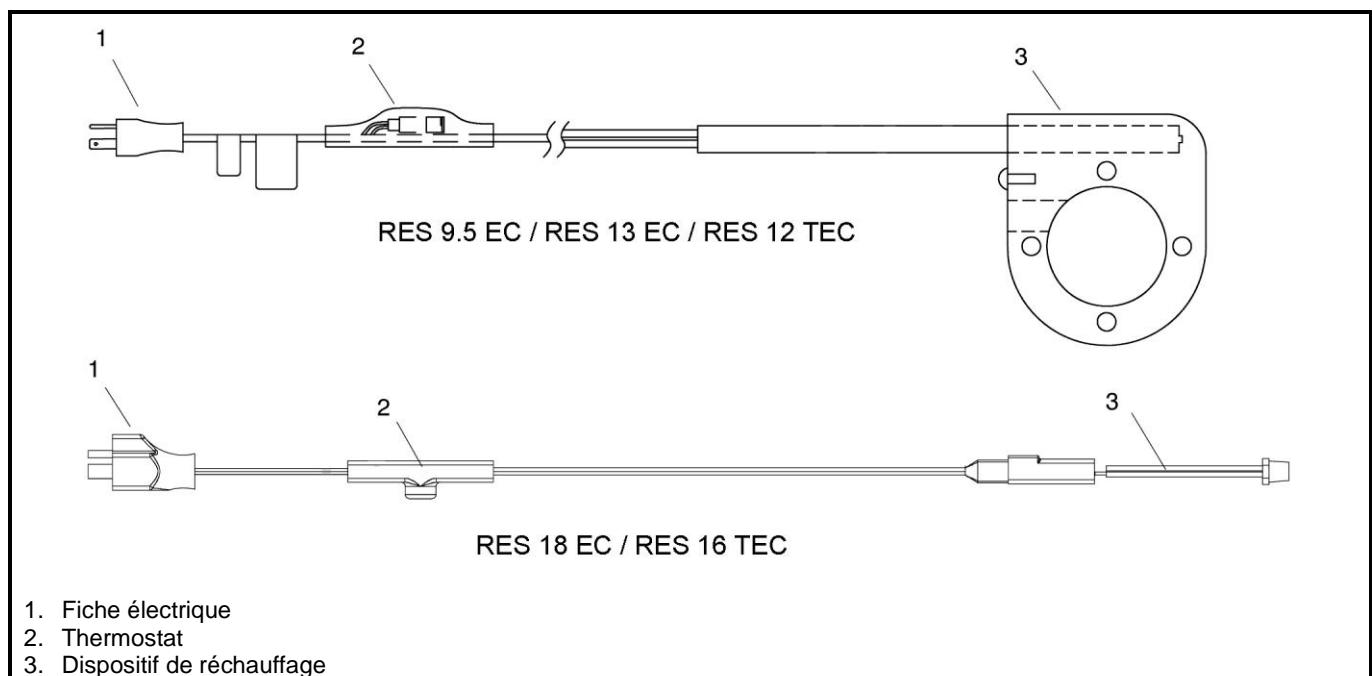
Dispositifs de réchauffage du carburateur avec thermostat intégré
